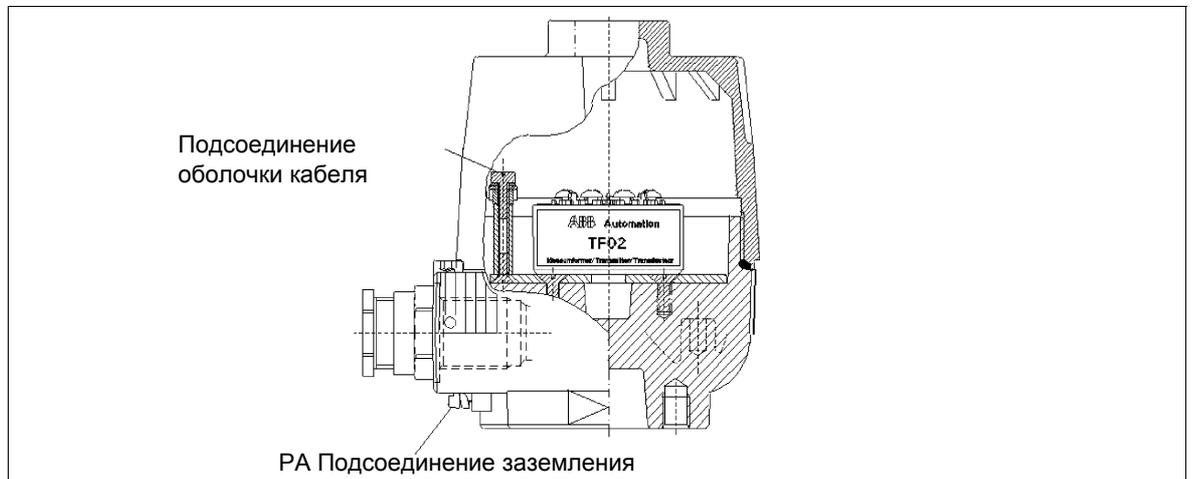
Детальный чертеж TF202 / TF202-Ex
